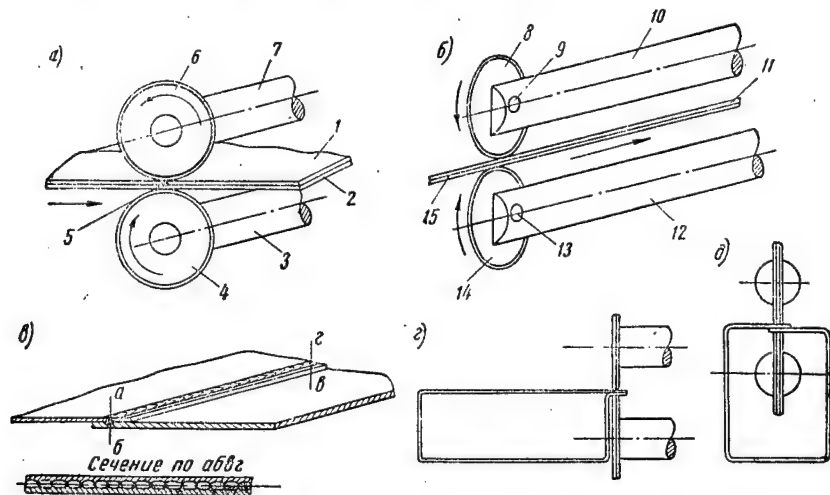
Схема шовной сварки: а — поперечная сварка; б — продольная сварка; в — сварное соединение; г — расположение трубы при поперечной сварке; д — расположение трубы при продольной сварке.
